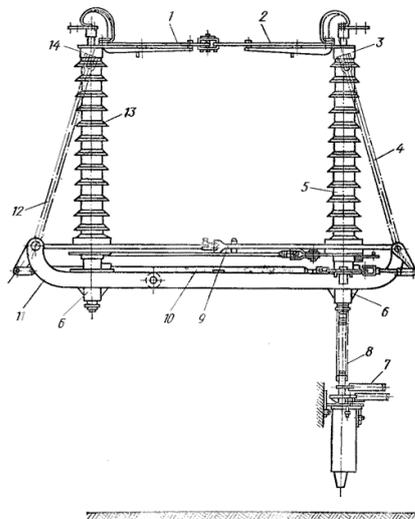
Разъединитель РЛНД2-110: 1, 2, 4 и 12 — ножи, 3 и 14 — неподвижные контакты, 5 и 13 — изоляторы, 6 — подшипники, 7 — привод, 8 — вал, 9 и 10 — тяги, 11 — перемычка
